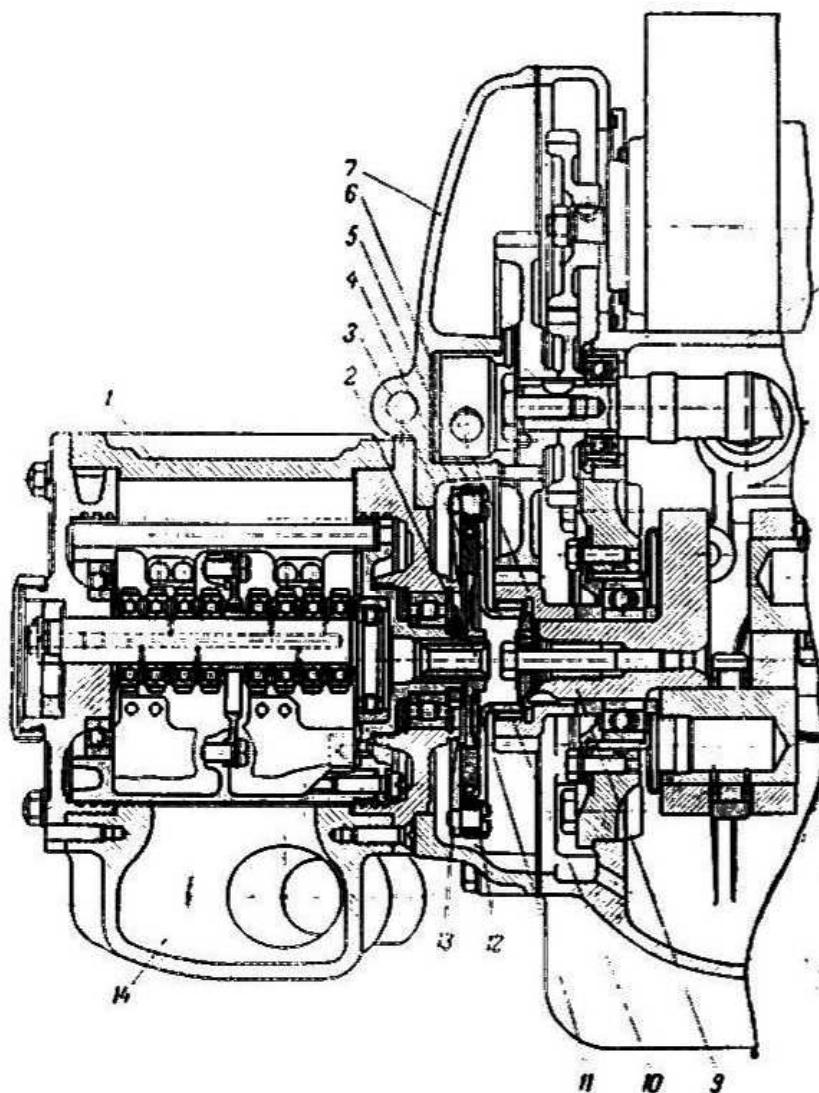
Разрез двигателя и нагнетателя М-35К:
